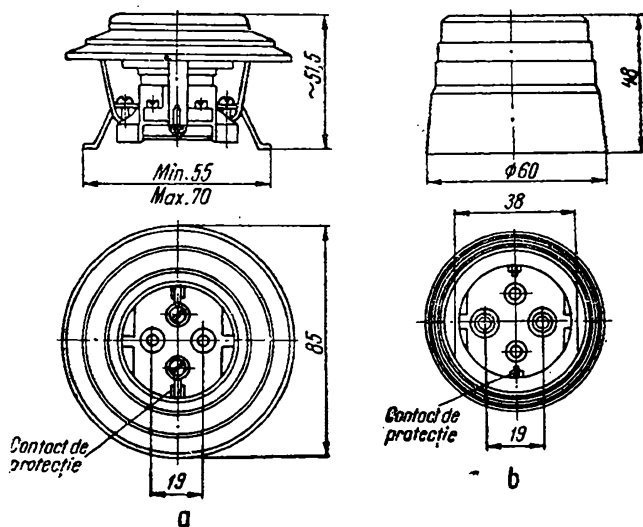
Priză bipolară cu contact de protecție pentru montaj:
